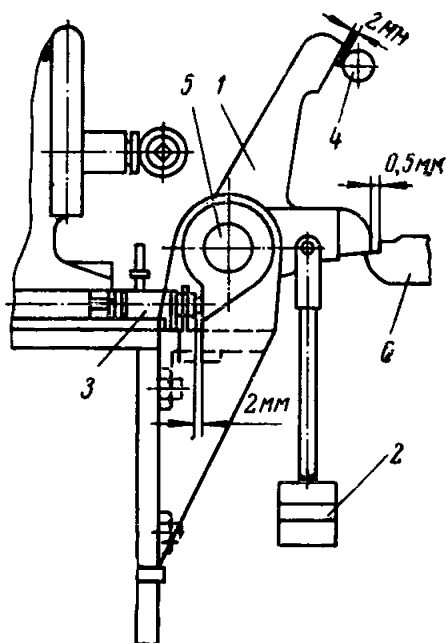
Запорное устройство зубчатого рычажного механизма перестановки:
